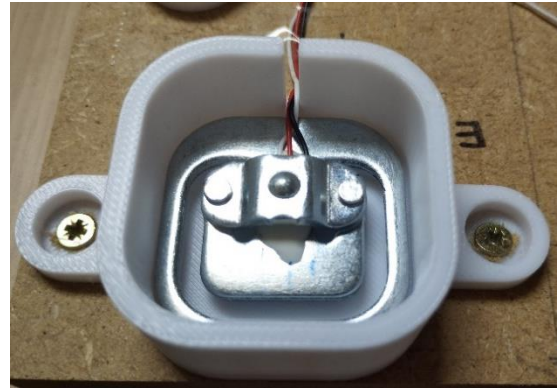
Paso 2 del montaje de los soportes. Fuente: Primaria.
